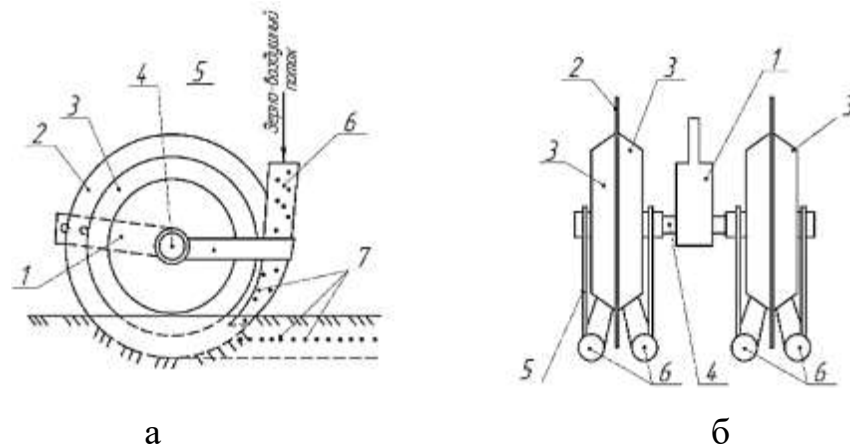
Технологічна схема роботи дводискового чотирирядкового сошника з усічено-конусними ребордами та нульовим кутом атаки дисків: а – вид збоку; б – вид зверху; 1 – корпус; 2 – диск; 3 – реборда; 4 – вісь; 5 – пластина; 6 – насіннепровід; 7 – насіння.
